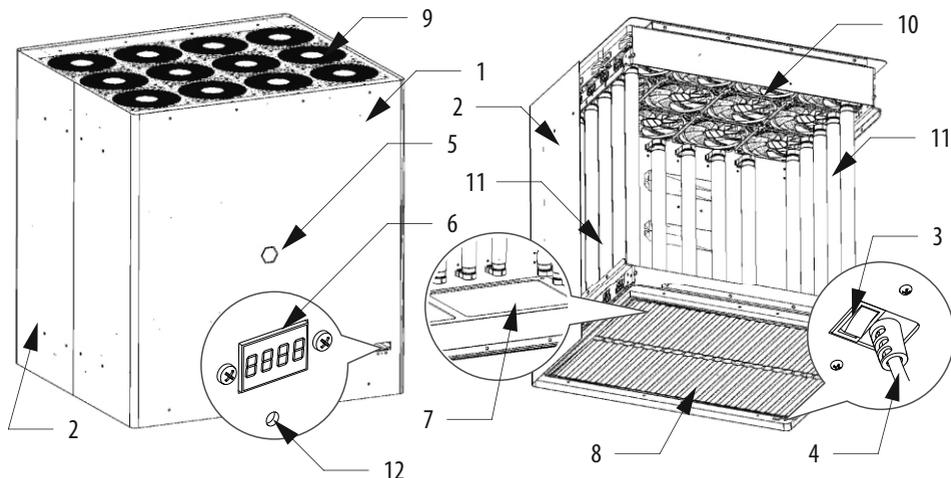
Общая конструкция рециркулятора ОВУ-33-116, ОВУ-33.1-116.
